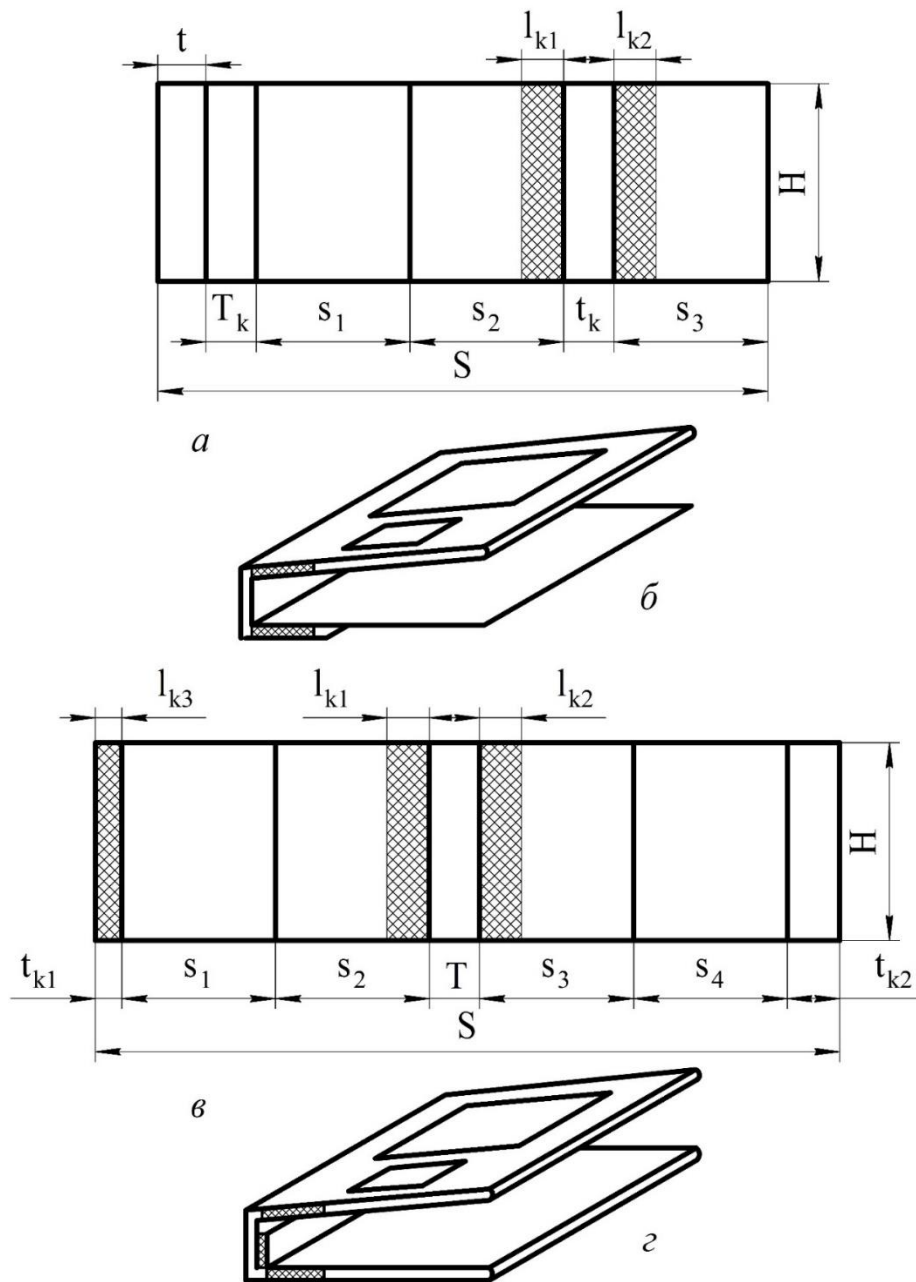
Обкладинки з подвійною просторовою конструкцією, виготовлені з однієї деталі
